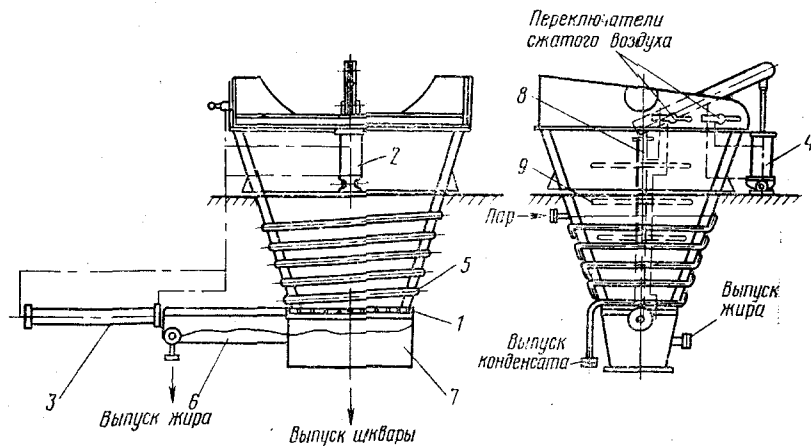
Отцеживатель с механизированной выгрузкой шквары фирмы «Атлас»:
